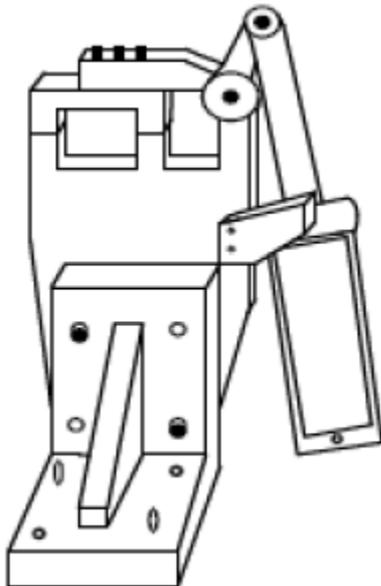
Welding locator fabrication flow process
